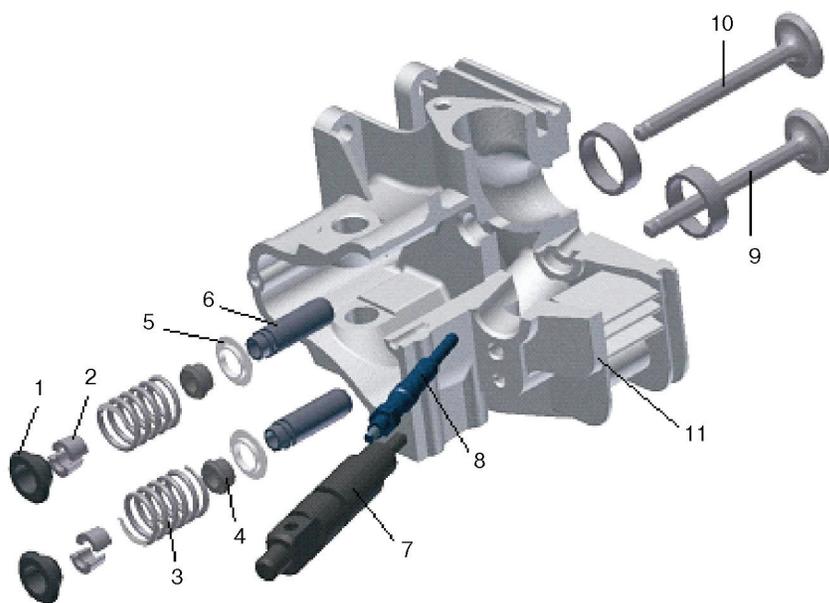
Трехмерные модели деталей головки двигателя МД-8 с воздушным охлаждением:
